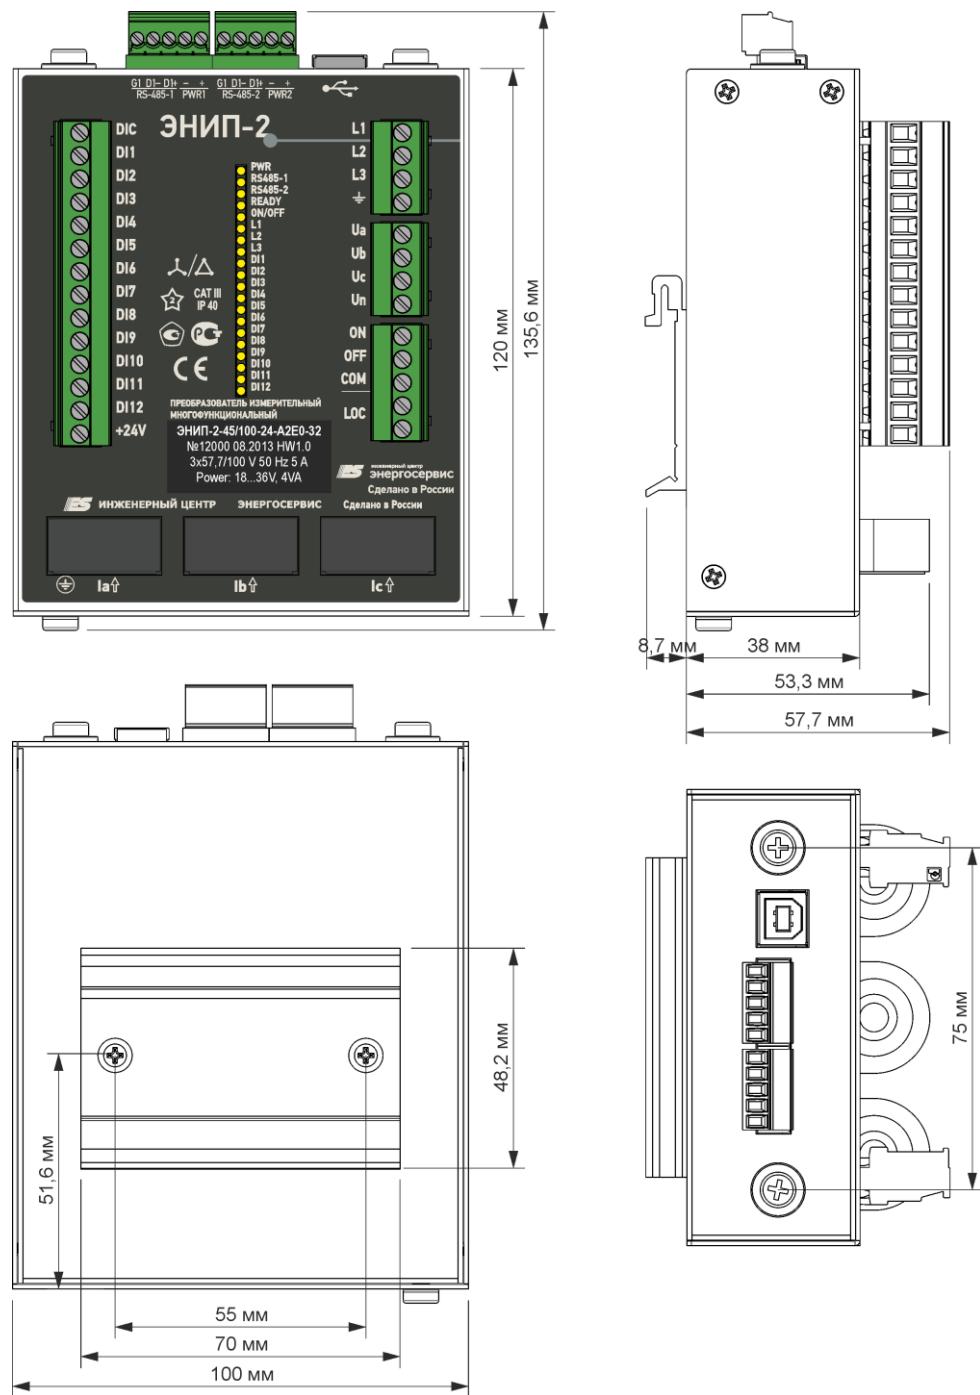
Габаритные размеры преобразователя ЭИП-2-...-32 (лицевая панель модификации ЭИП-2-45/100-24-A2E0-32)
